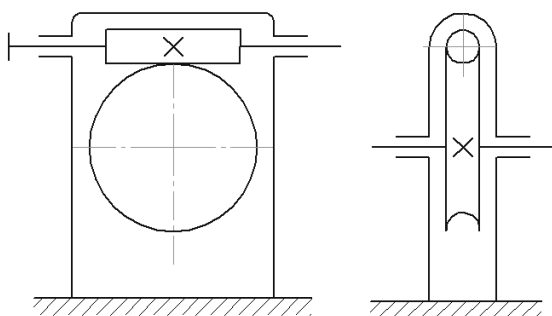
Одноступенчатый горизонтальный червячный редуктор с верхним расположением червяка
